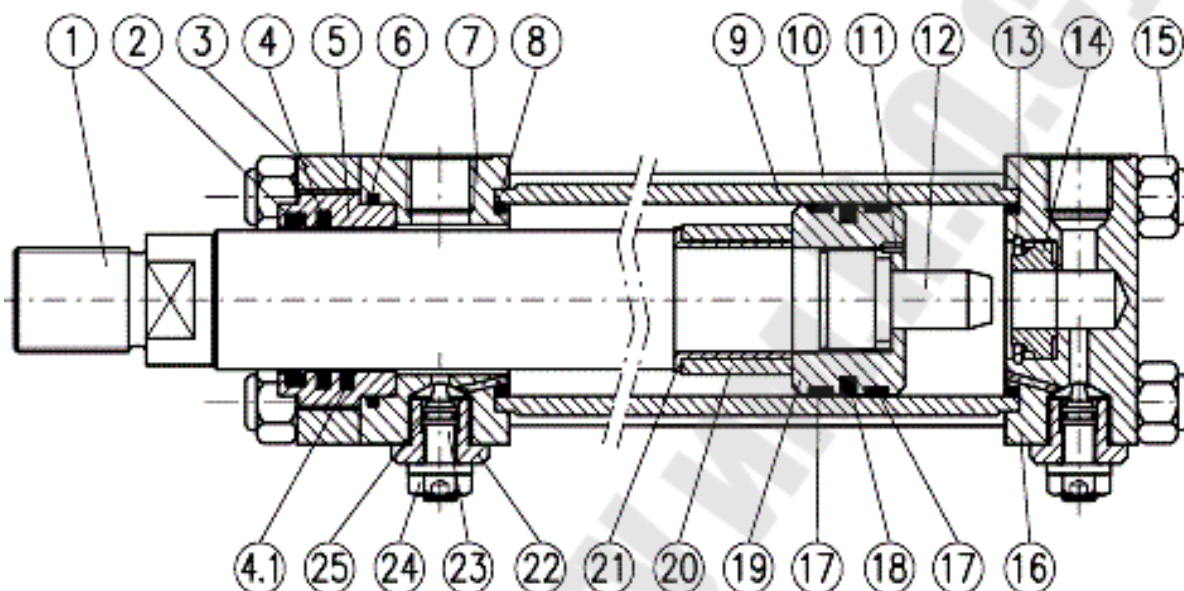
Конструкция гидроцилиндра типа СК: 1 – шток; 2 - грязеуловительную манжету; 3 – фланцы; 4 - уплотнения штока; 5 - направляющую втулку; 6 - уплотнительное кольцо; 7 - штоковую крышку; 8 – гильзу; 9 – шпильку; 10 – штифт; 11 - плунжер поршневого демпфера; 12 - стопорное кольцо; 13 - заднюю втулку демпфера; 14 – гайку; 15 - поршневую крышку; 16 - направляющую втулку; 17 - уплотнение поршня; 18 – поршень; 19 - поршневой демпфер; 20 - упорную втулку; 21 - корпус дросселя; 22 - регулировочный винт; 23 – контргайку; 24 - уплотнительное кольцо
